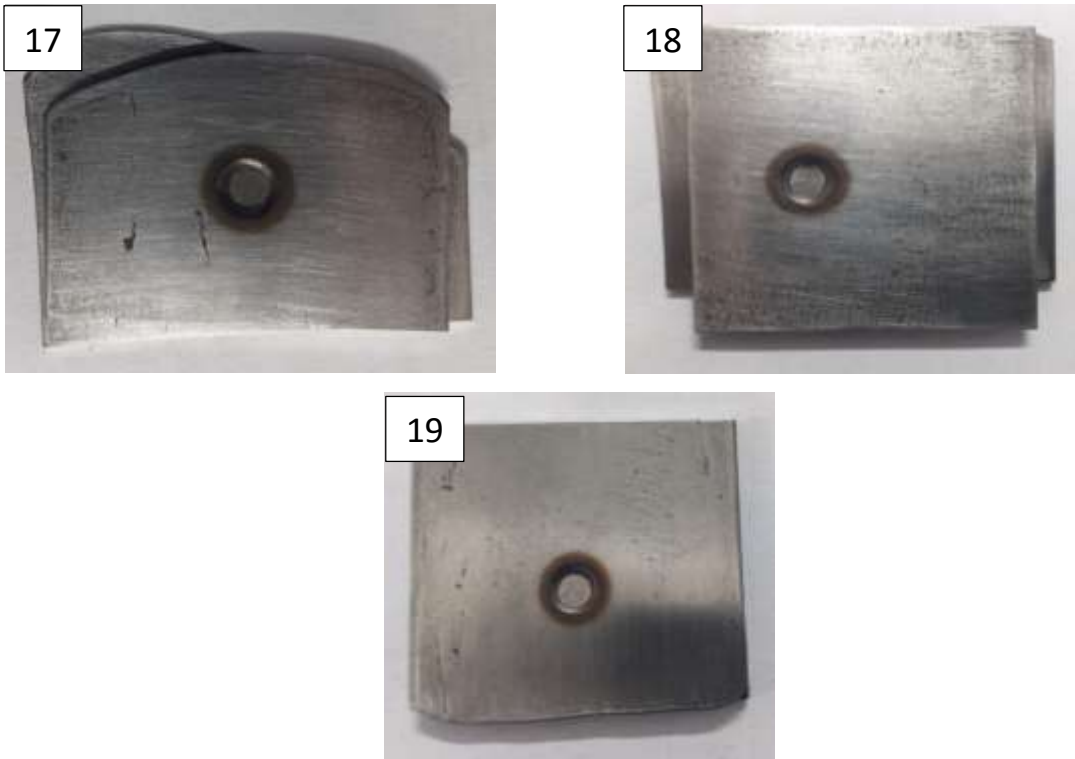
Botones de soldadura obtenidos en el tercer grupo de pruebas.
